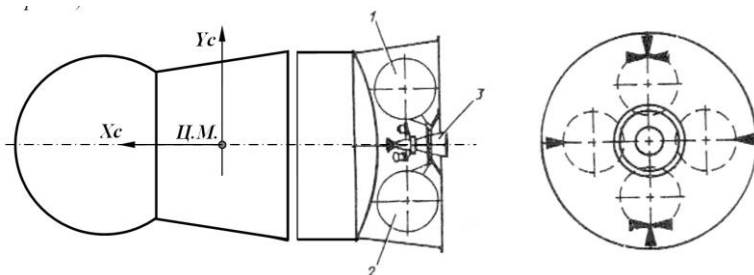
Пример расположения реактивной двигательной установки на КА (1- реактивный двигатель; 2 – топливный бак окислителя; 3 – топливный бак горючего)
